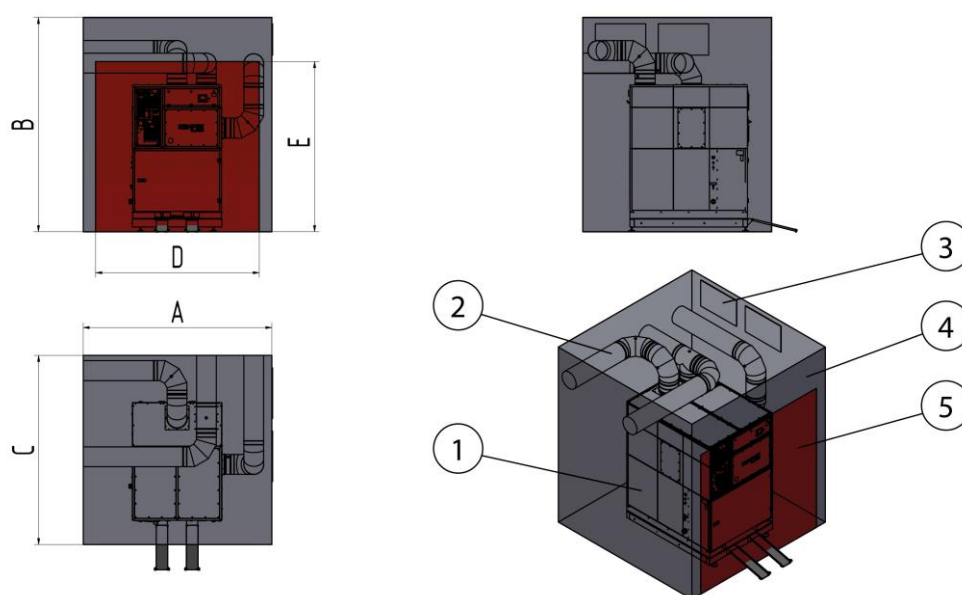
Estrutura de proteção – Variante exemplificativa 1
